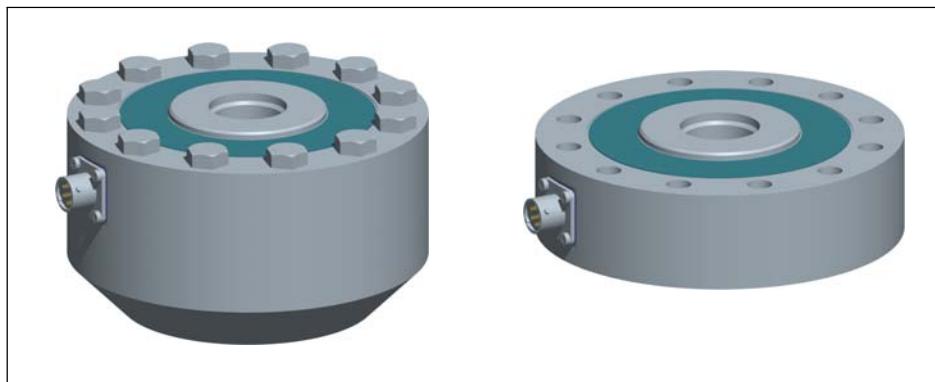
U10M mit Adapter (links) und ohne Adapter (rechts)
